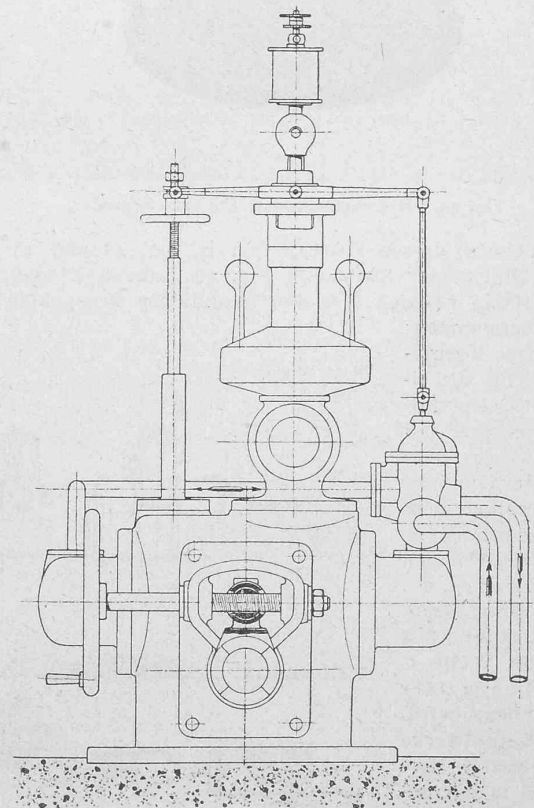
Schema des Regulators mit hydraulischem Hochdruck-Servomotor. Ansicht.
